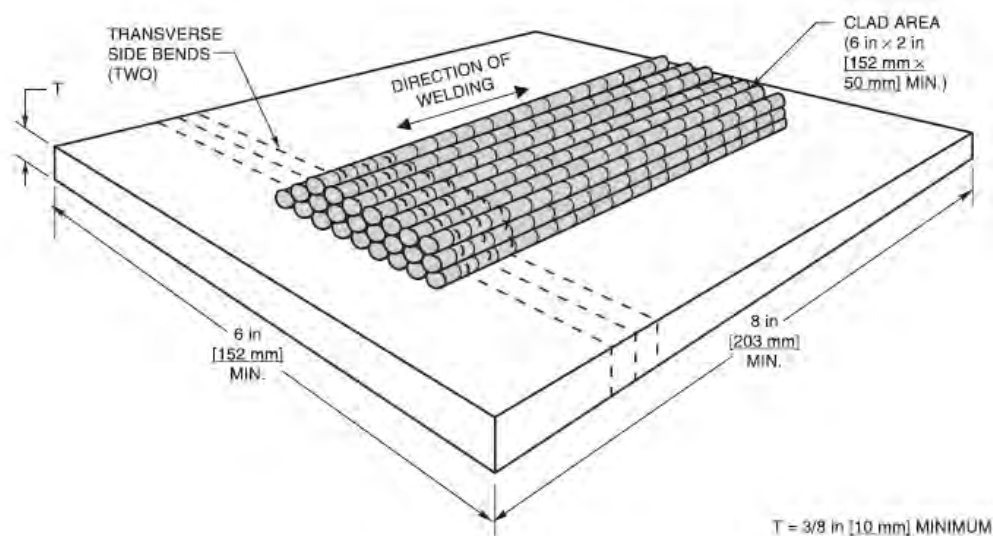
Diseño de junta para calificación del procedimiento (American Welding Society, 2009).
